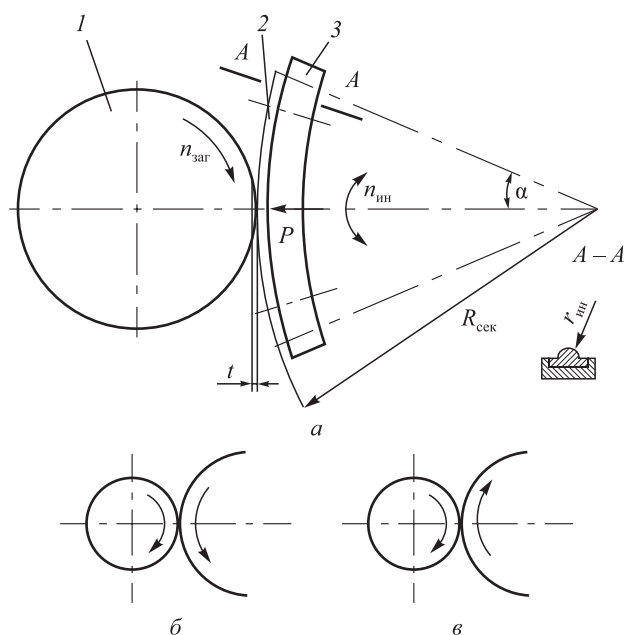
Схема маятникового поверхностного пластического деформирования (а):
